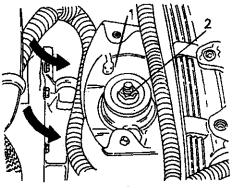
Крепление опоры подвески со стороны коробки передач. Скоба подвески (1) крепится на коробке передач гайкой (2). Стрелками показано расположение болтов крепления на консоли подвески.
